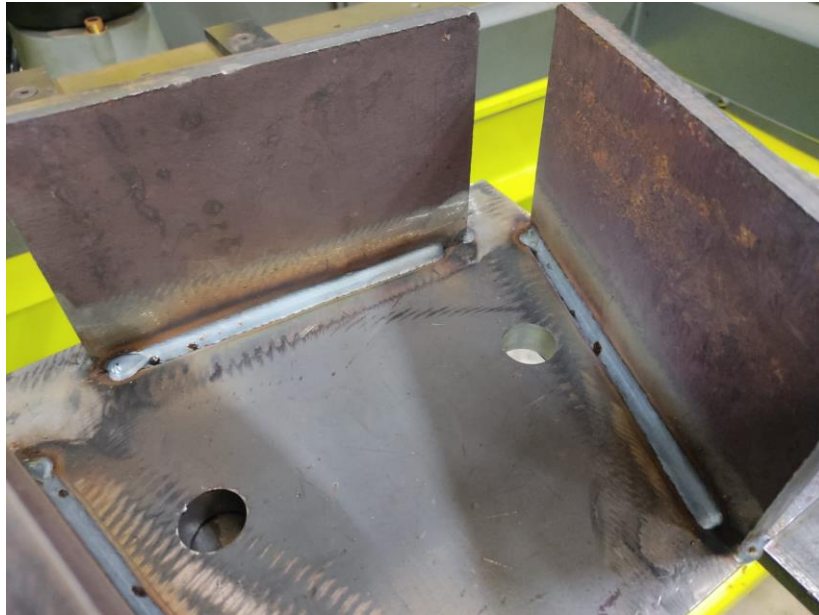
Cordões de soldadura realizados pelo robô FANUC na Motofil
